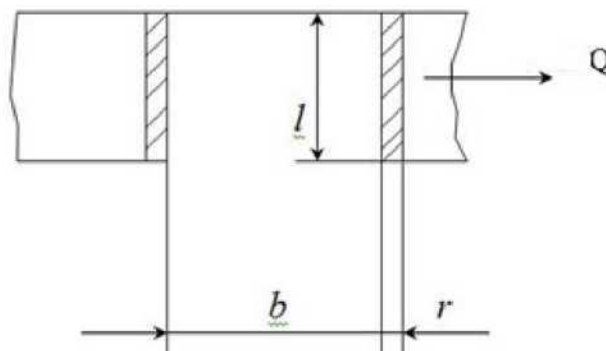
Схема к расчету сварного соединения
